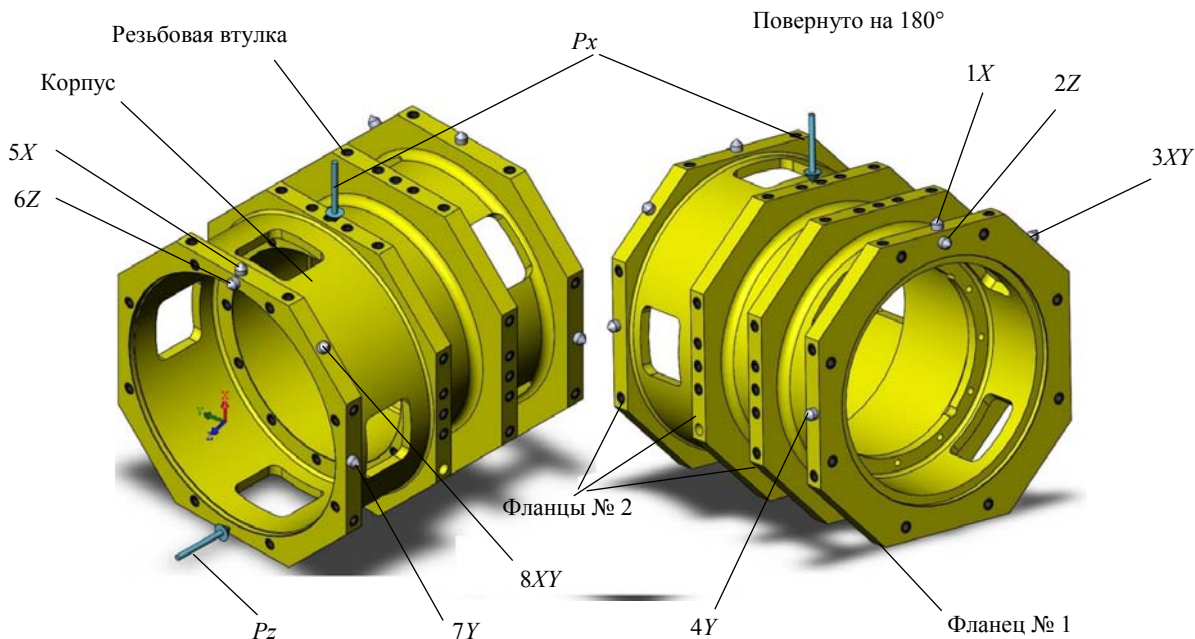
Модель корпуса, места приложения нагрузки и установки пьезоакселерометров
